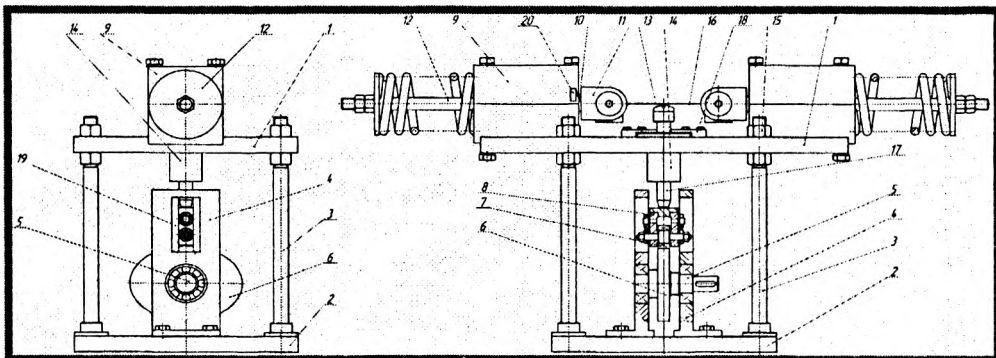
Схема установки для ускоренных испытаний ленточных пил
